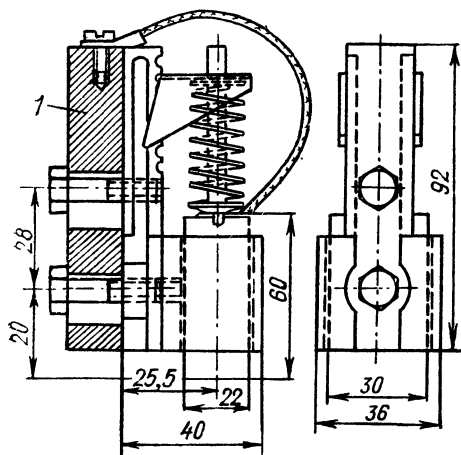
Щеткодержатель для двигателя с контактными кольцами
